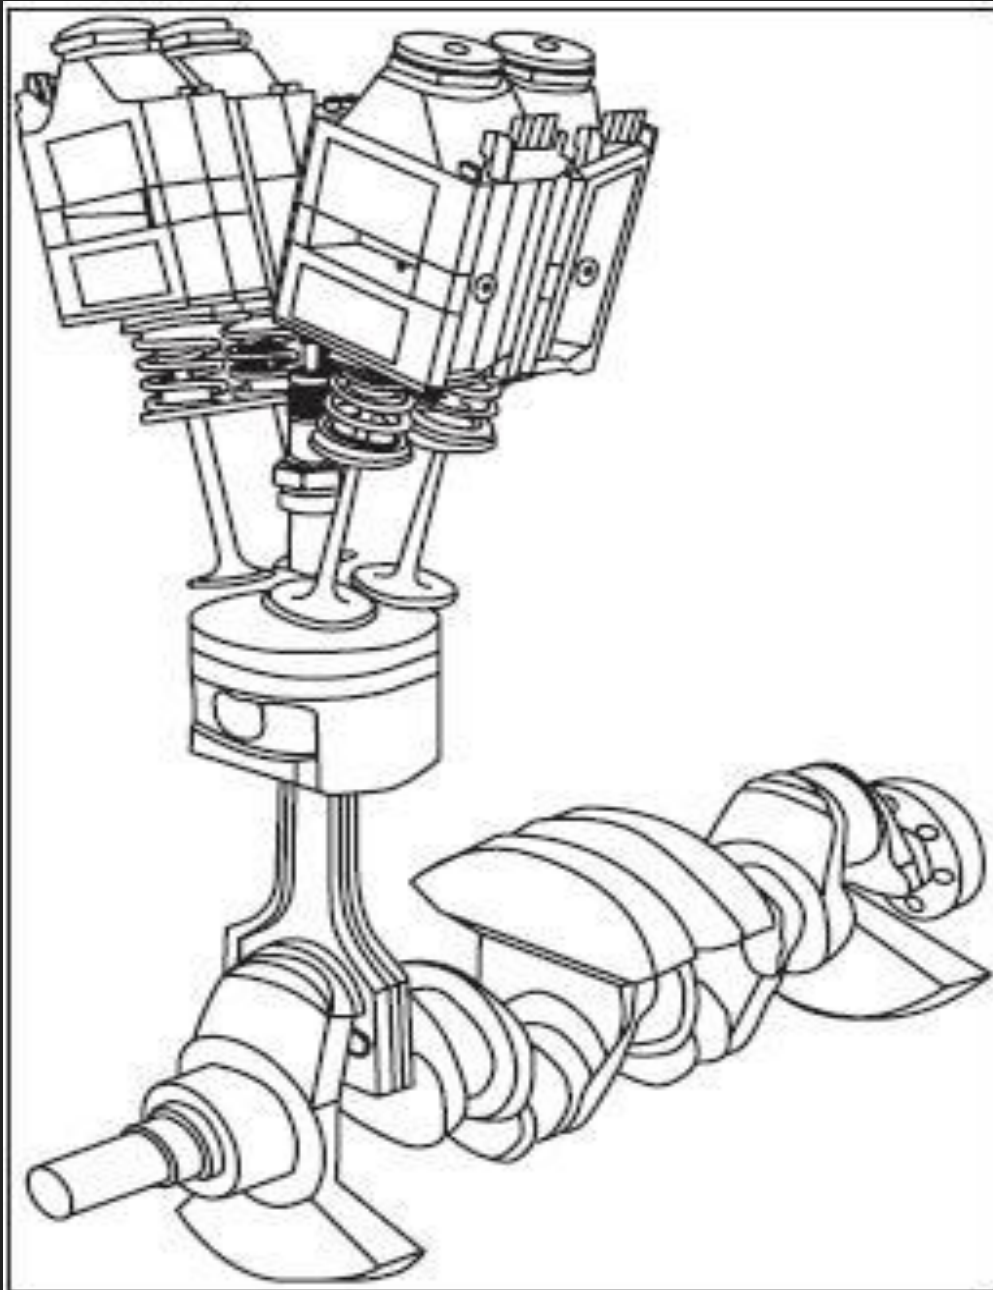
Внешний вид и компоновка электромагнитного привода ГР-клапанов
